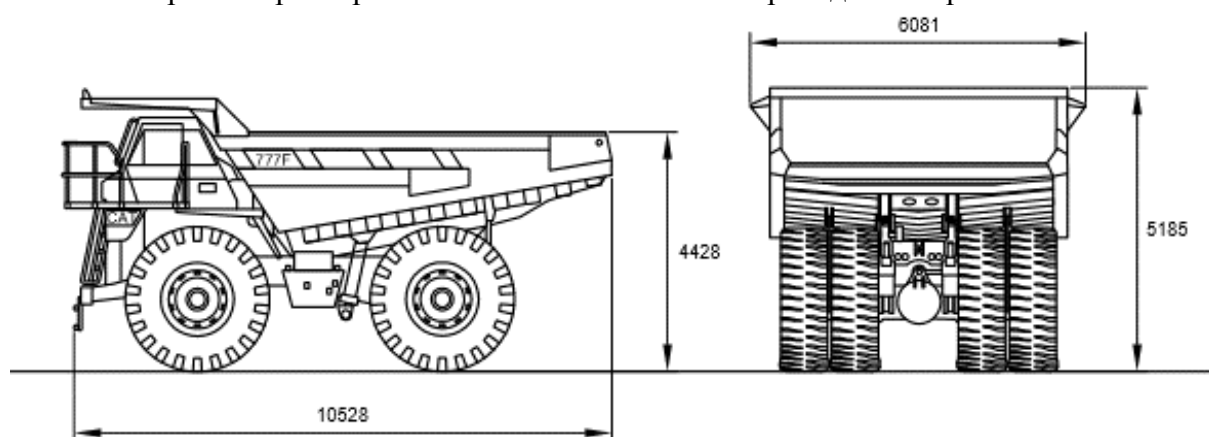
Габаритные размеры автосамосвала CAT 777F
